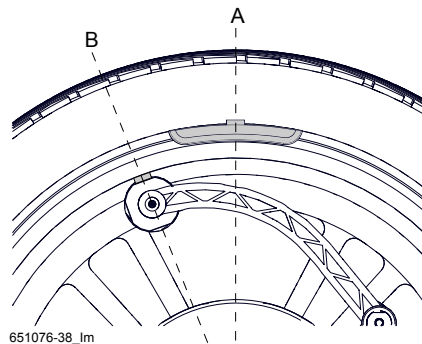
Klebegewicht mit elektronischem Messschieber anbringen
